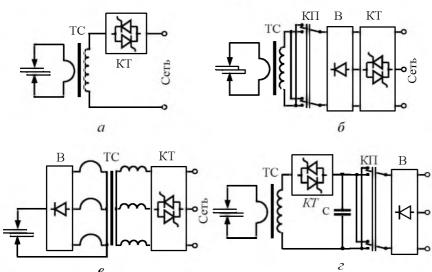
Структурные силовые схемы машин контактной сварки: ТС — силовой сварочный трансформатор; КТ — контактор (тиристорный); В — выпрямительный блок; КП — коммутирующий переключатель; С — блок конденсаторов
